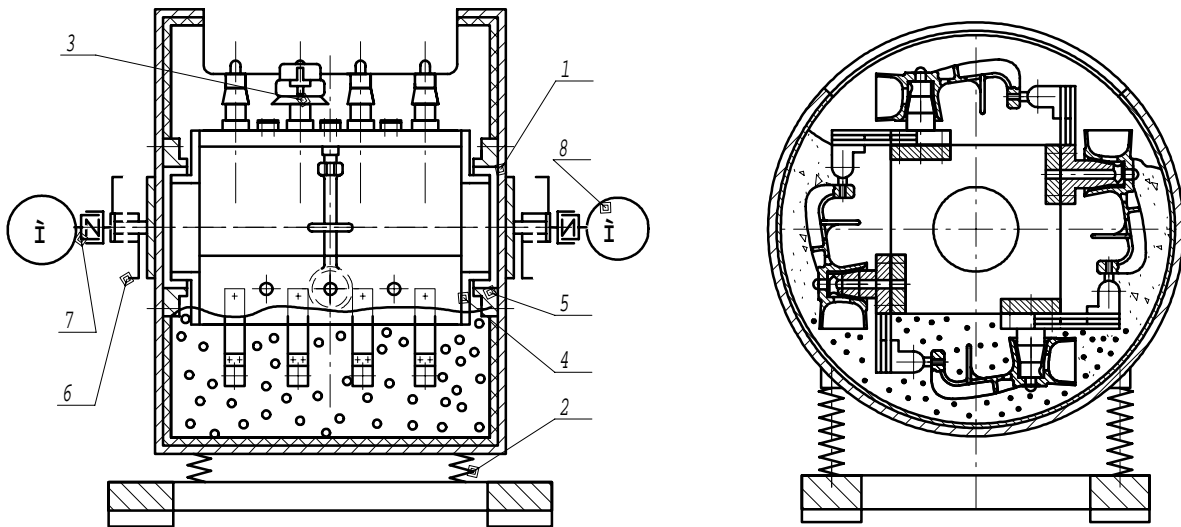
Конструктивні схеми машин з обертовим пристроєм для обробки деталей:
